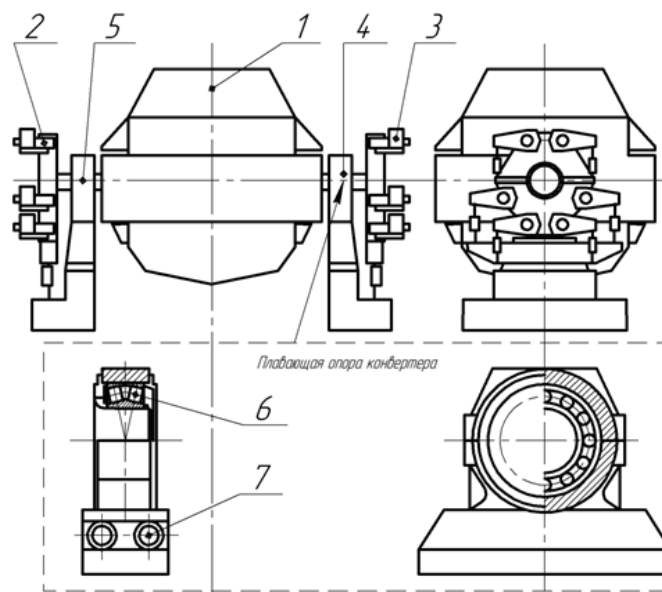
Кислородный конвертер: 1 – груша конвертера; 2 – привод конвертера левый; 3 – привод конвертера правый; 4 – фиксированная опора конвертера; 5 – плавающая опора конвертера; 6 – опорный подшипник; 7 – шарнирный узел плавающей опоры конвертера
